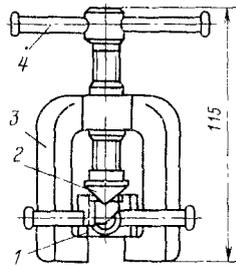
Приспособление для развальцовки медных труб ПРМТ-10 (винтовое)
